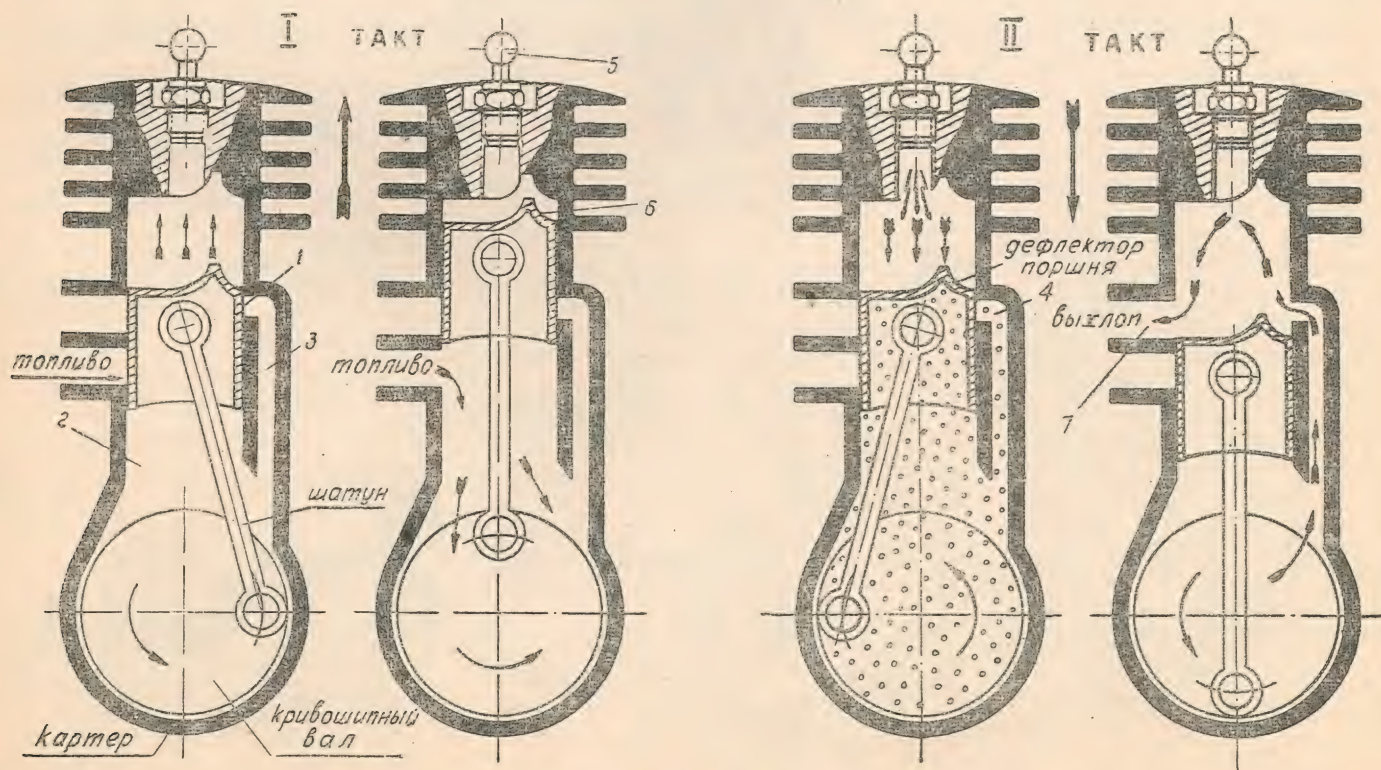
Рабочий цикл двухтактного двигателя внутреннего сгорания.
